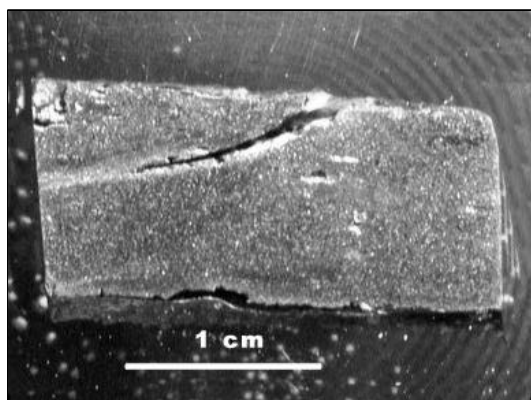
Macrografía de la zona de soldadura de la pieza.
